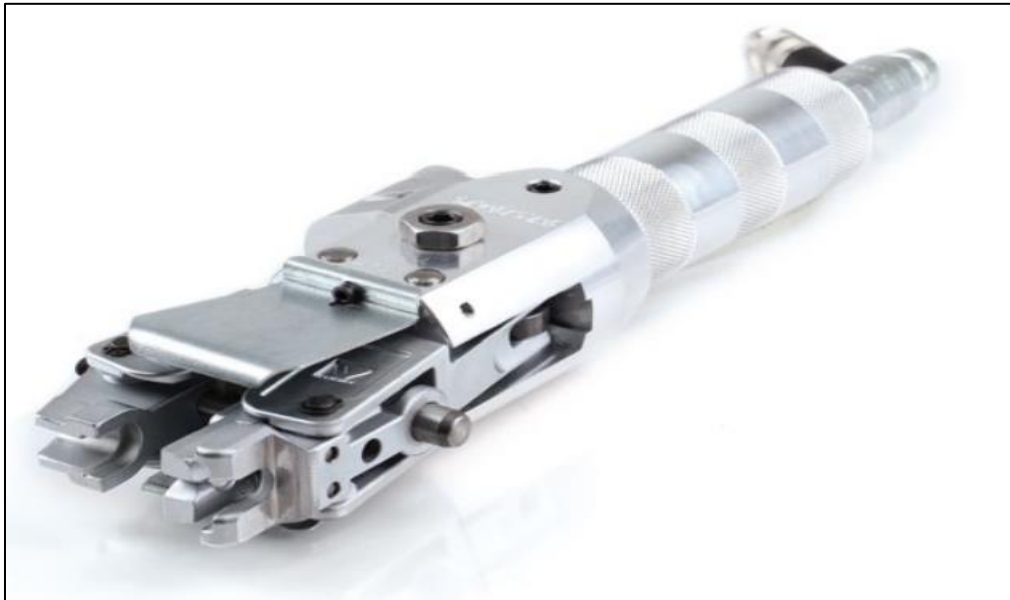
Herramienta hidráulica de montaje LOKRING. Fuente: vulkan.com
